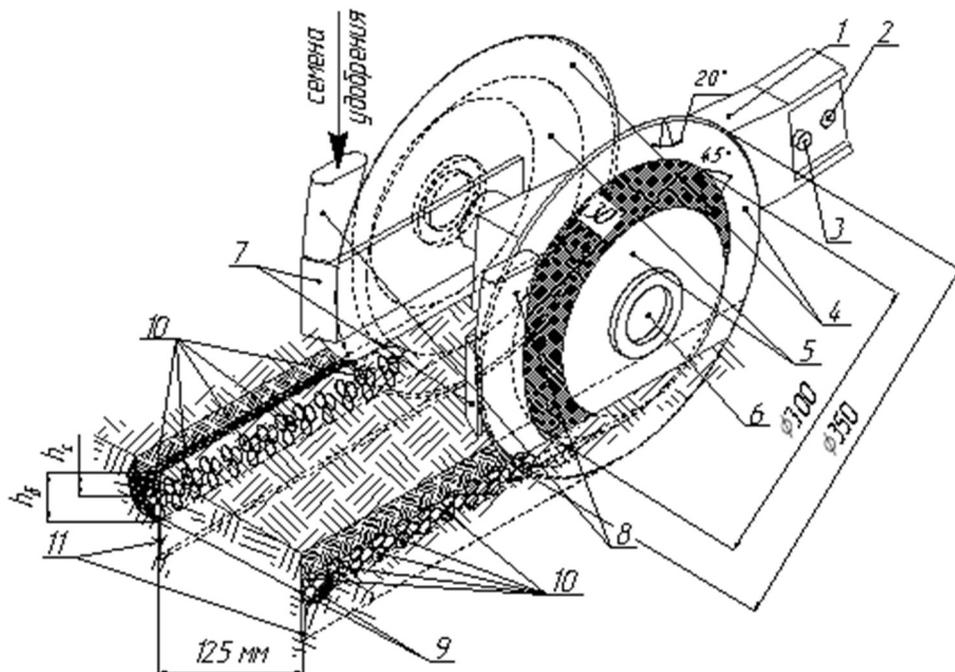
Конструктивно-технологическая схема работы двухдискового сошника с нулевым углом атаки дисков и внешними усеченно-коническими ребрами-бороздообразователями: 1 – корпус; 2, 3 – отверстия с болтами для крепления к поводку сеялки; 4 – плоские диски; 5 – усеченно-конусные ребра-бороздообразователи; 6 – оси; 7 – пластина; 8 – семянаправитель; 9 – бороздка; 10 – семена и гранулы стартовой дозы фосфорных удобрений; 11 – уплотненное ложе; h_b – глубина бороздки; h_c – глубина укладки семян
